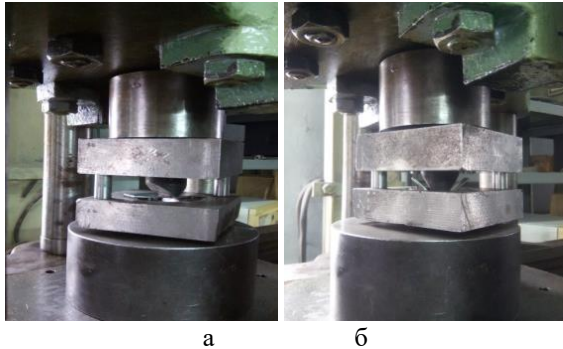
Гидравлический пресс с установленным гибочным штампом: а – для изгиба на 90°; б – для изгиба на 120°
